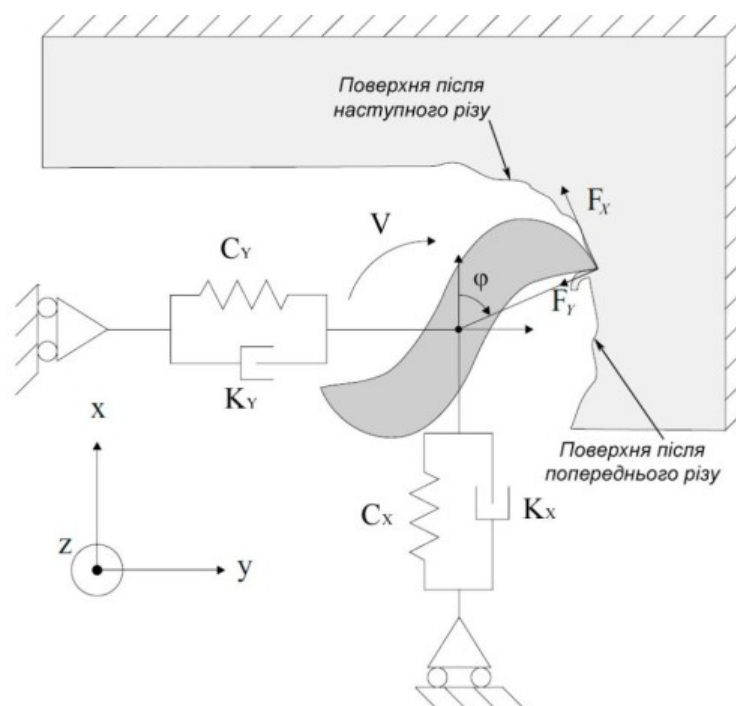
Схема для розрахунку регенеративних автоколивань інструменту при фрезеруванні
